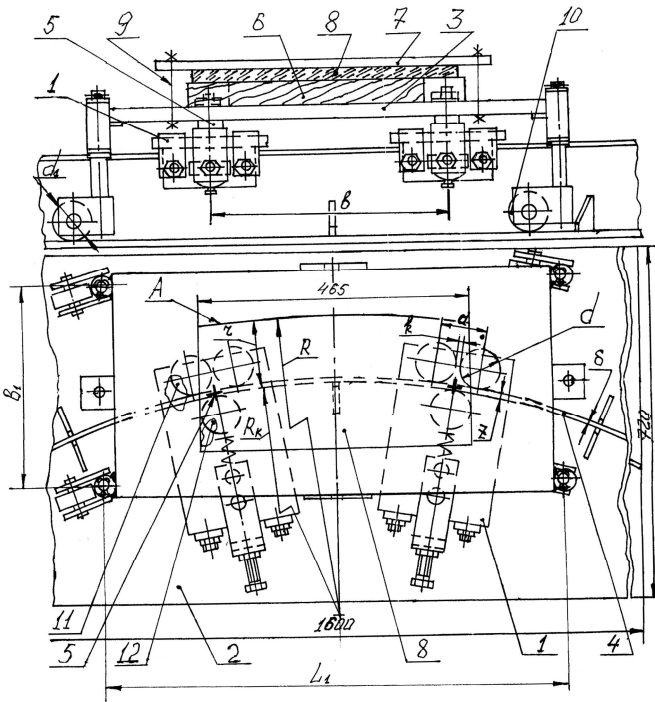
Схема конструкції моделі: 1 – поворотний демпферний пристрій; 2 – нерухома основа; 3 – рухомий робочий стіл; 4 – копір-колія; 5 – ось повороту; 6 – дерев'яна прокладка; 7 – фіксуєча планка; 8 – кам'яна заготовка; 9 – деталі кріплення; 10 – опорний каточок (рухома опора); 11 – опорний ролик; 12 – натискаючий ролик
